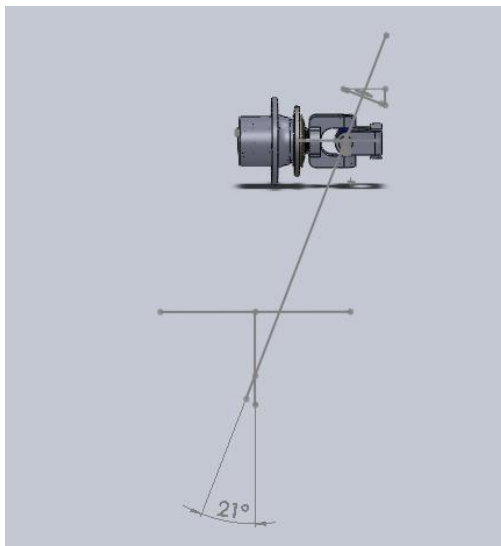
Esboço de dimensões conjunto de pneu e roda
